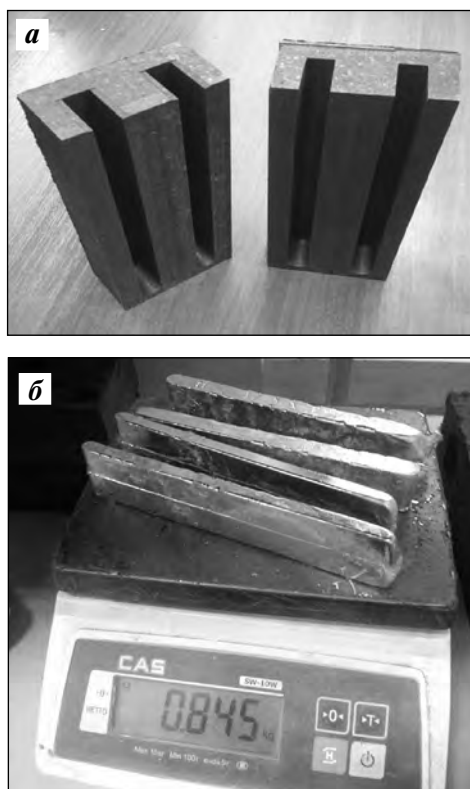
Внешний вид графитовой формы (а) и отливок сплава (б)
